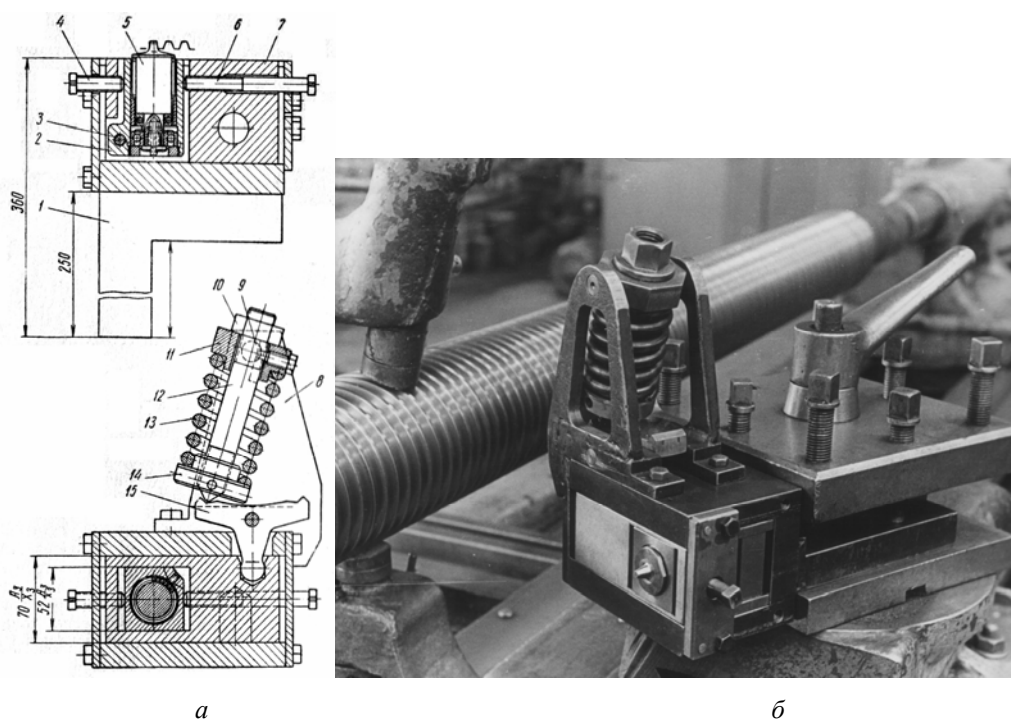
Схема (а) и общий вид (б) устройства для обкатывания трапецеидальных резьб и червяков с шагом 8... 16 мм
